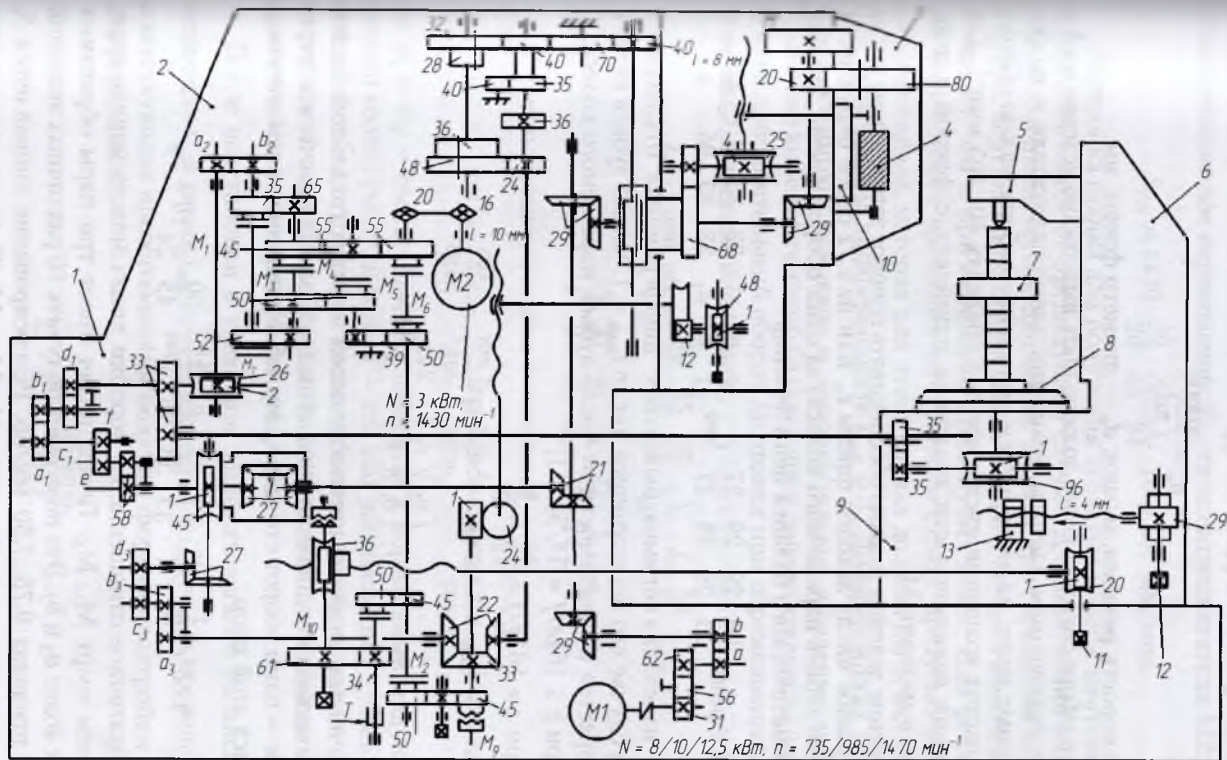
Кинематическая схема зубофрезерного станка мод. 53A50:
